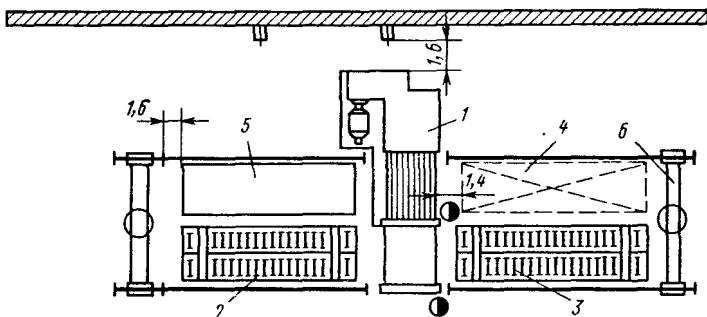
Схема планировки оборудования листопрямительной машины
